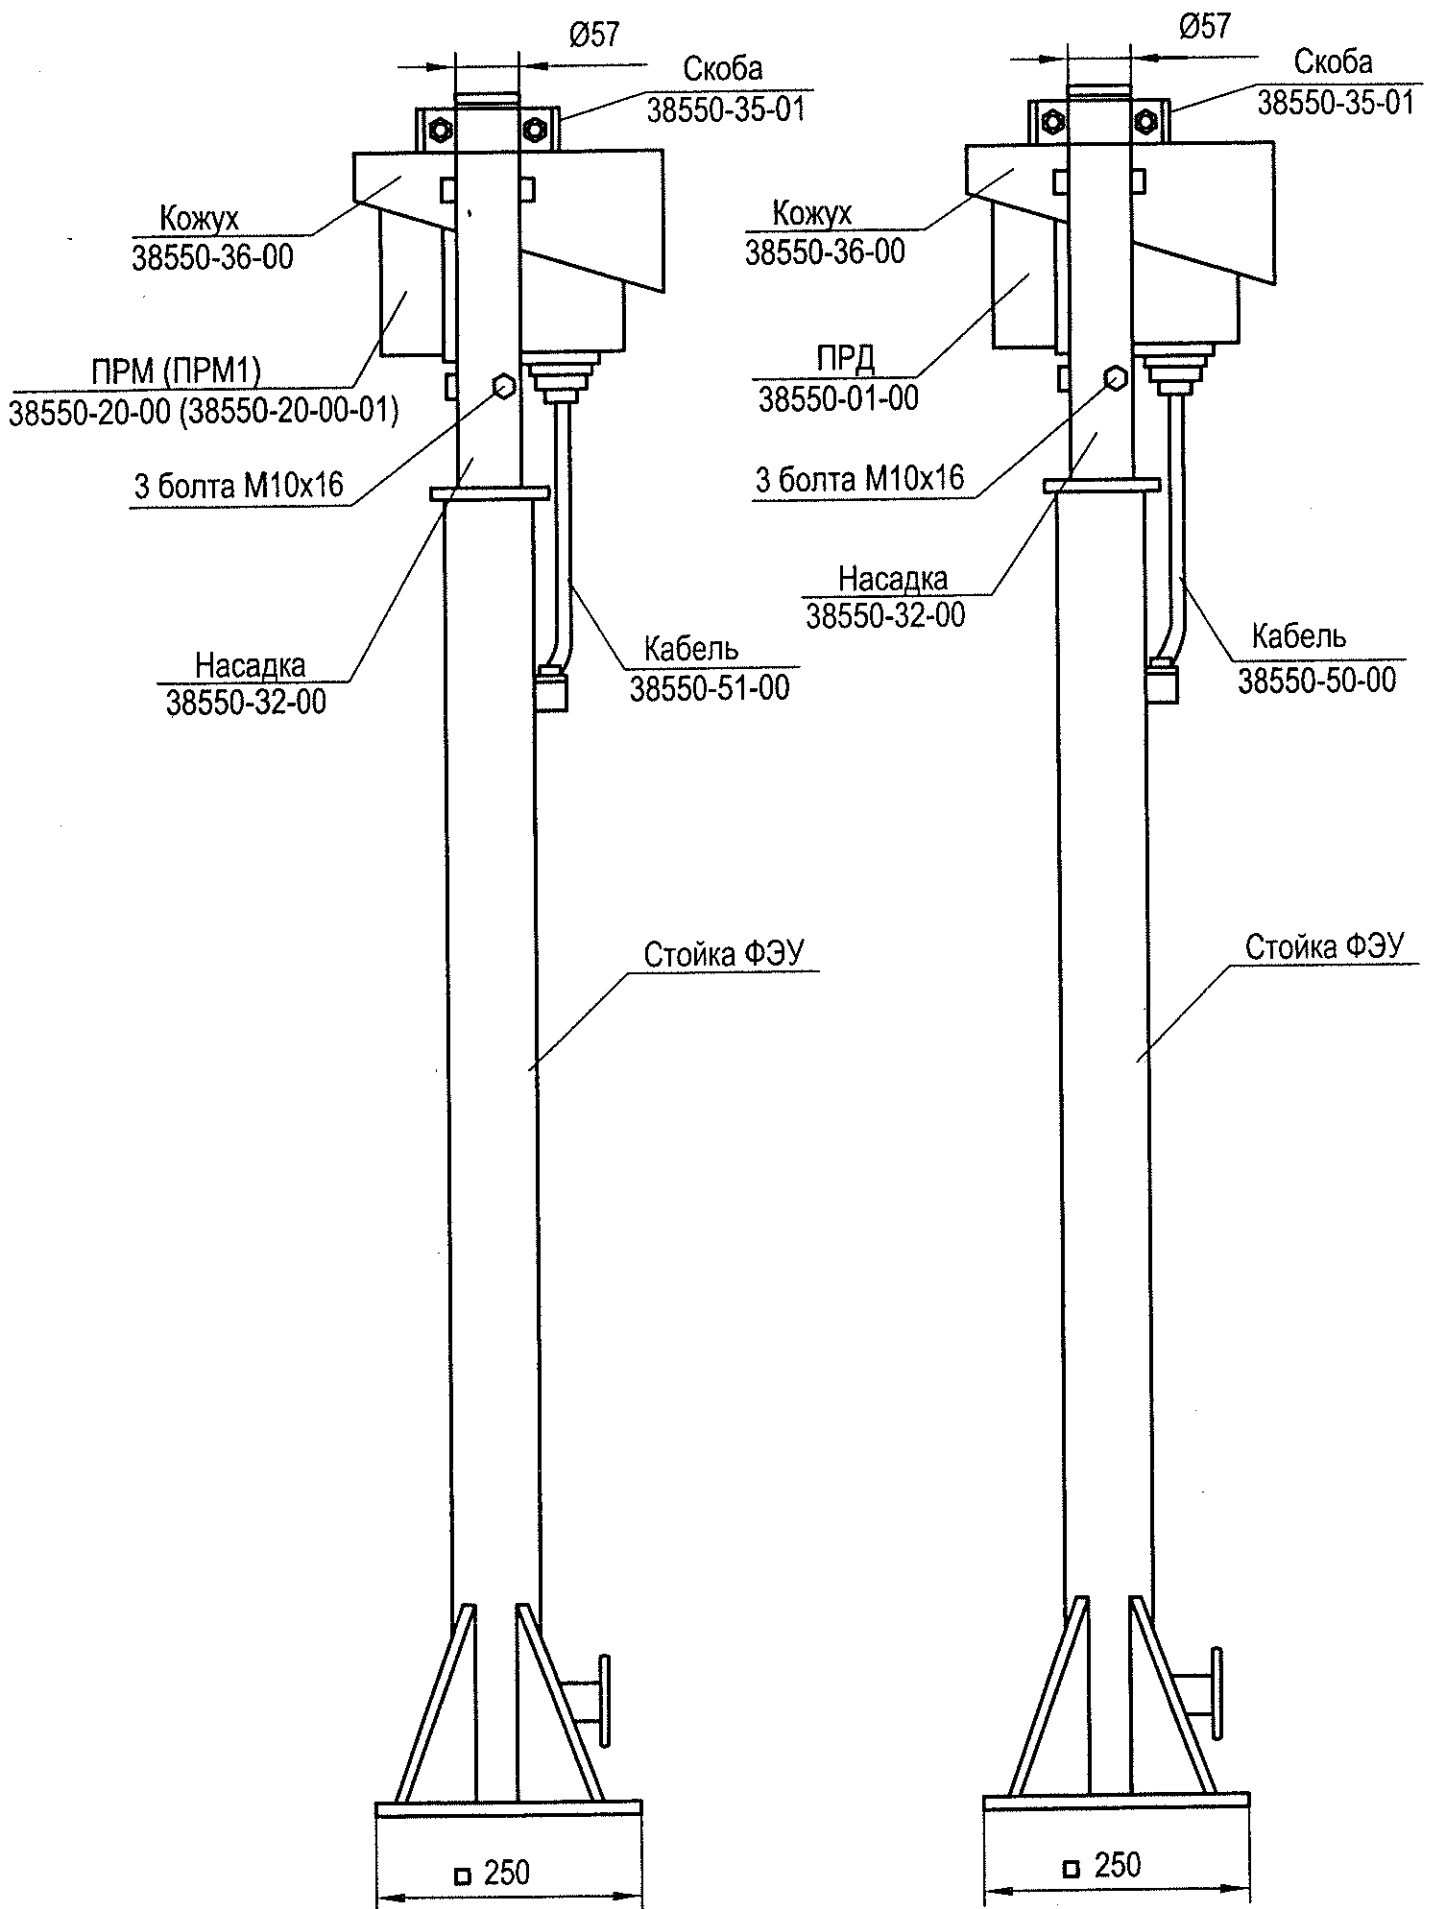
Установка ПРД или ПРМ (ПРМ1) на стойке ФЭУ с помощью насадки.
